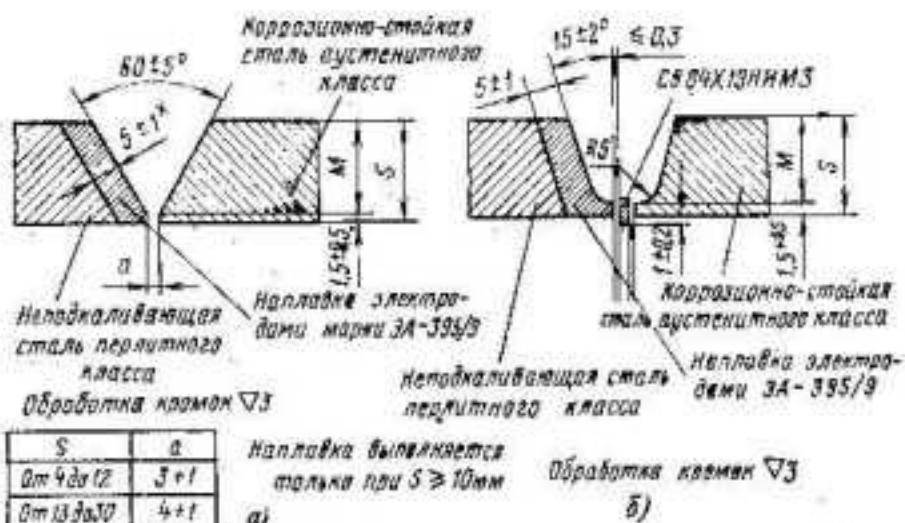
Подготовка кромок двухслойных сталей к комбинированной сварке.
